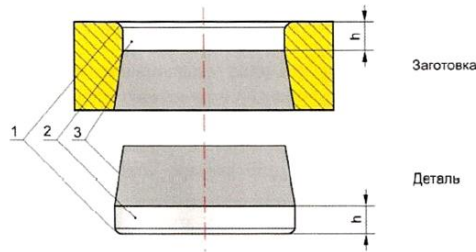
Характерные участки боковой поверхности детали и заготовки после вырубki
